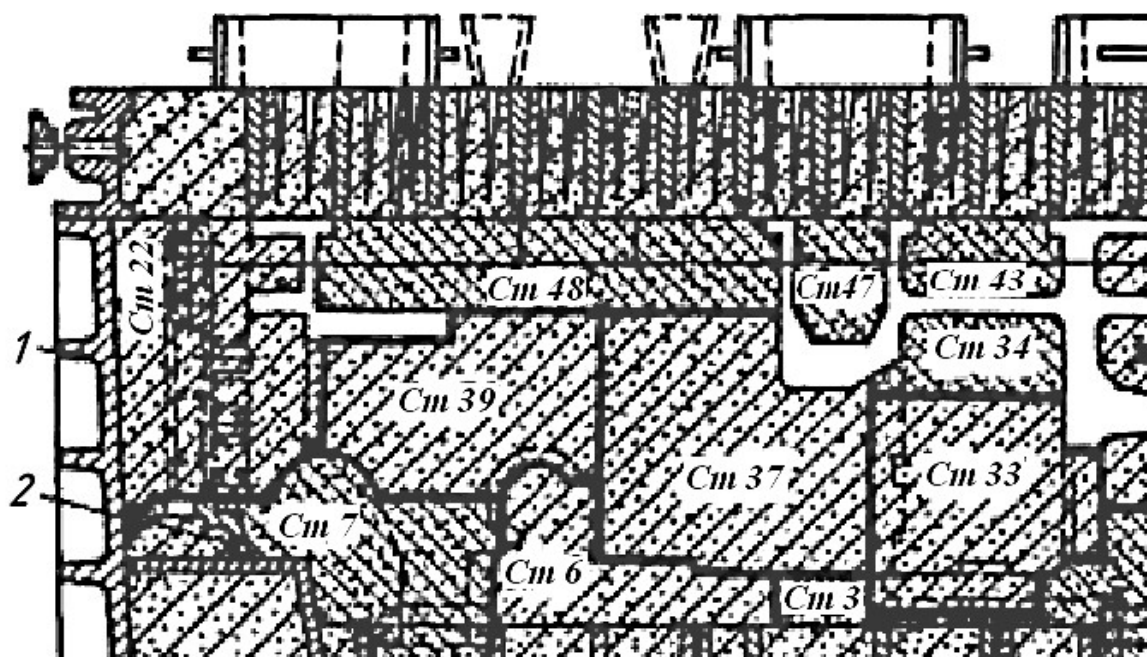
Схема формовки в жакетах станины горизонтально-ковочной машины
